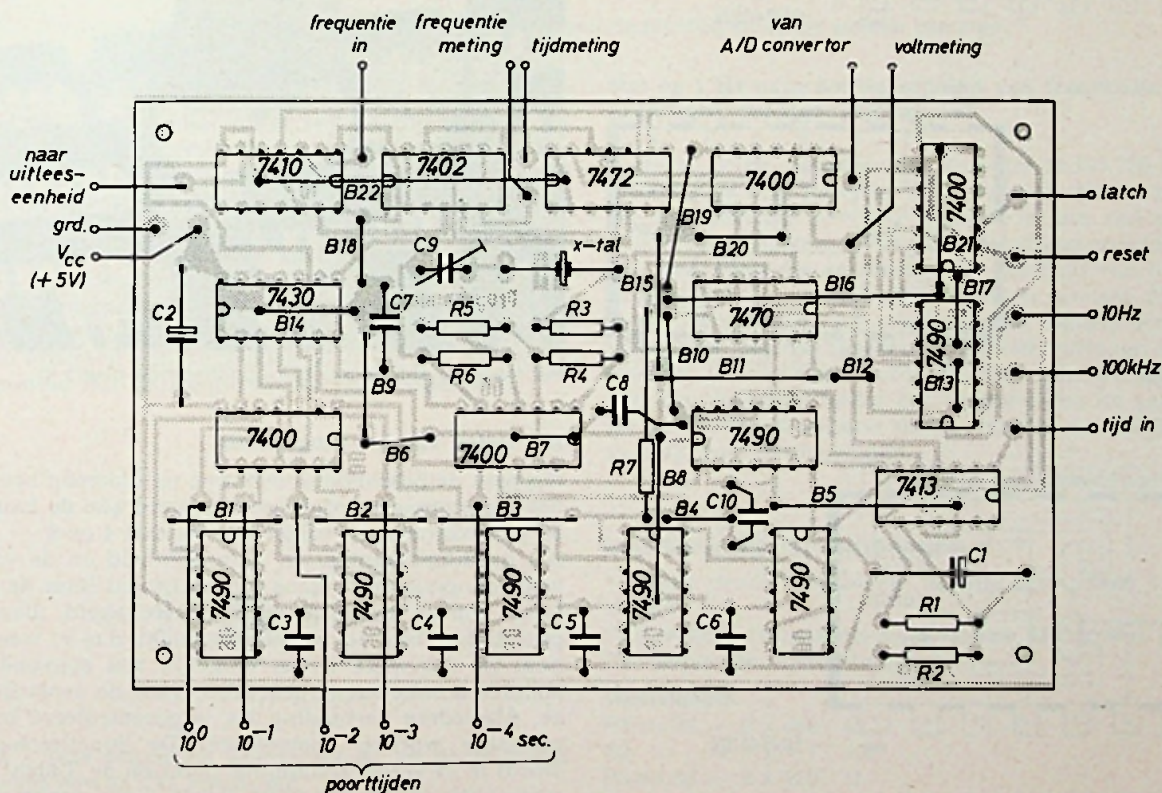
Componentenopstelling. Vergete geen draadbruggen ! D1 en C11 onder de print solderen
